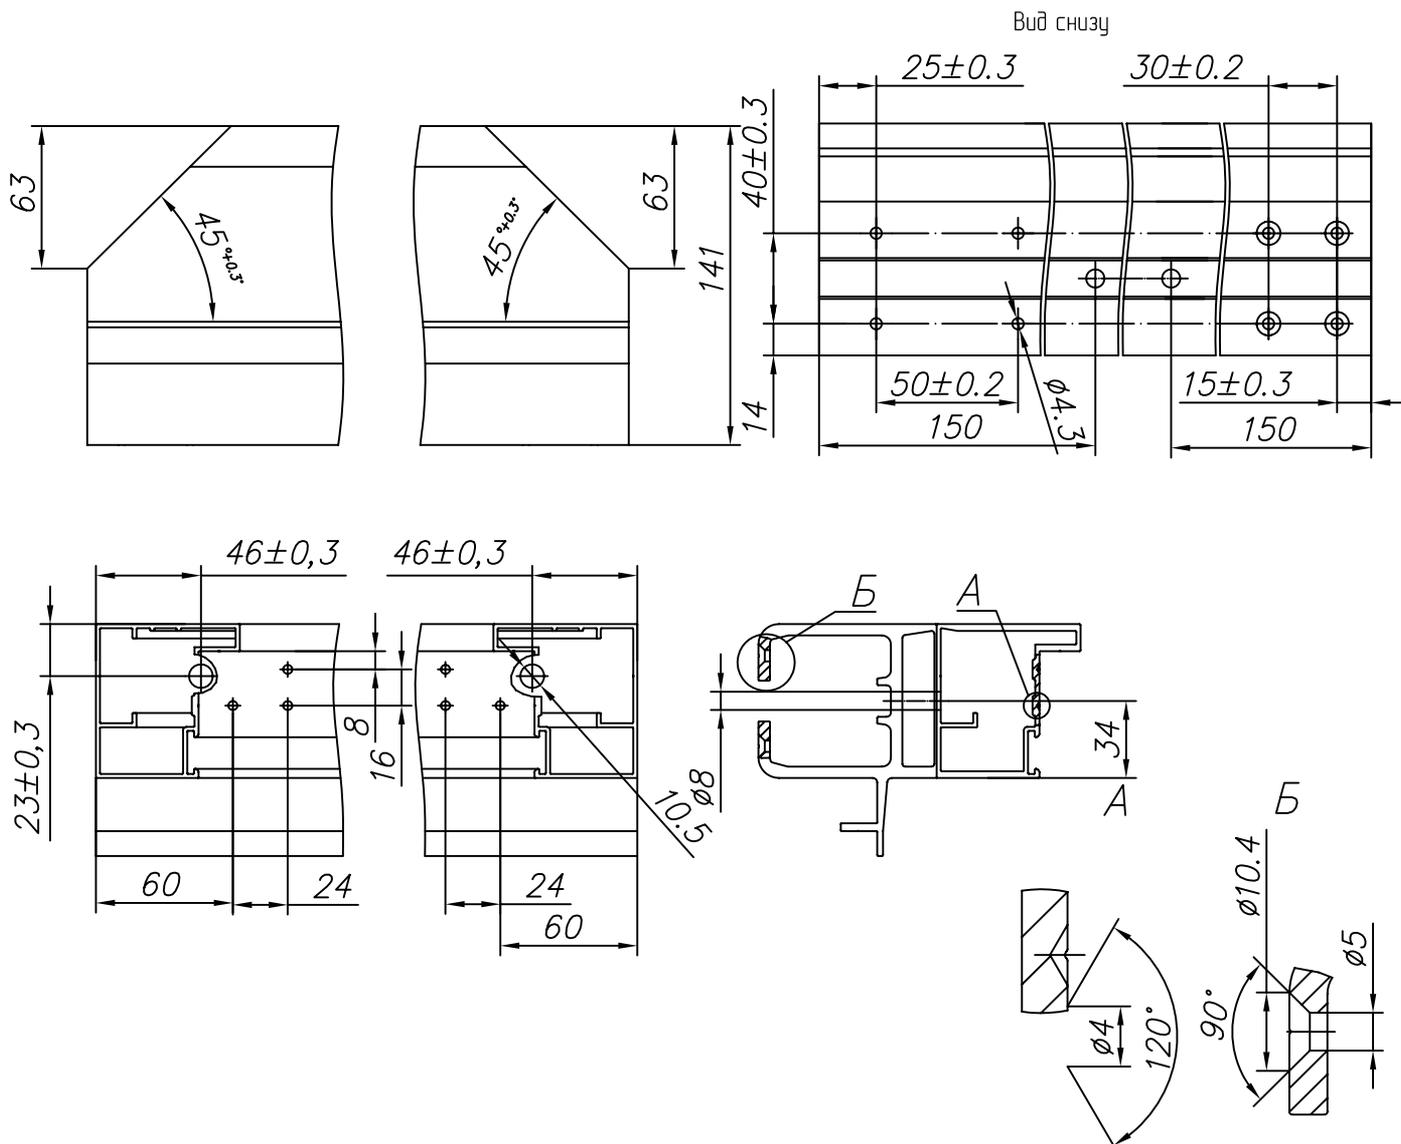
Изготовление шины для пассивной(опорной) створки (открытие вправо)
